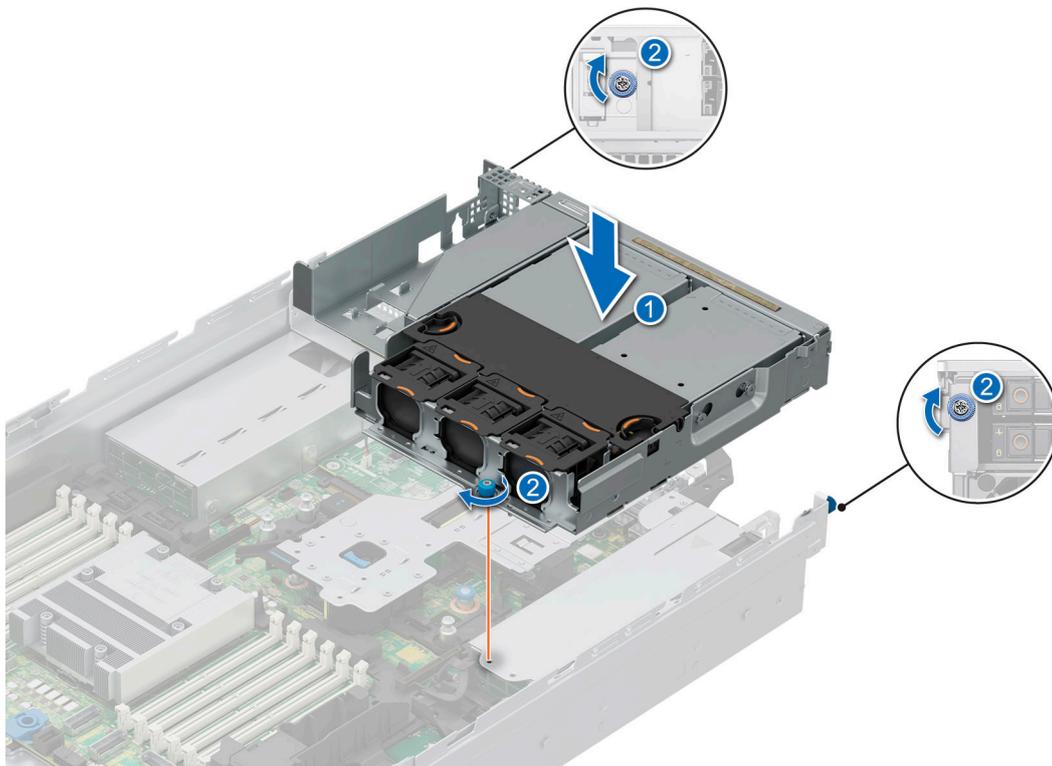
Installation du module de disques arrière 4 x 2,5 pouces
